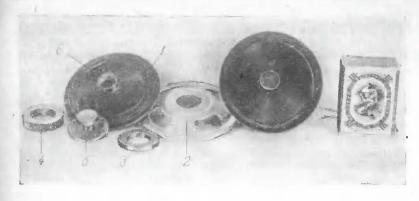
Внешний вид громкоговорителя с кольцевой магнитной системой. 1 — диффузор; 2 — диффузородержатель; 3 — фланец; 4 — магнит; 5 — керн с фланцем; 6 — катушка.
